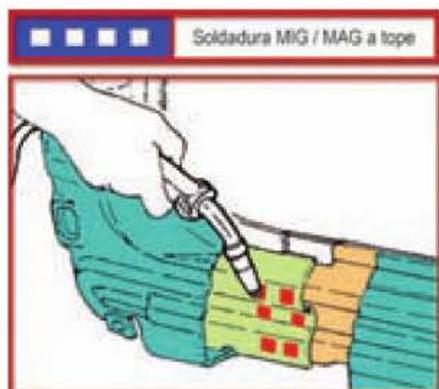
Pictograma de soldadura MIG/MAG a tope.
